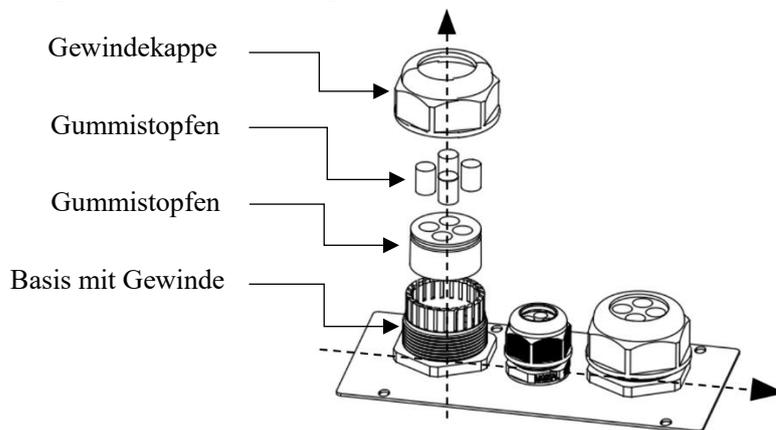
Innerer Aufbau der Fräsbohrung
